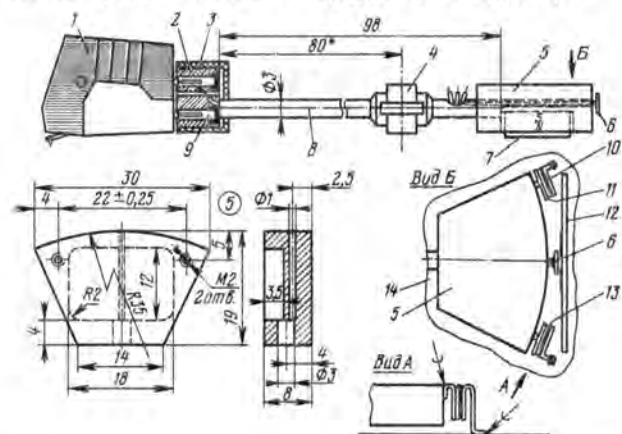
Звукоиндуктор: 1 — головка ГЗМ-003; 2 — пластина, стеклотекстолит фольгированный; 3 — колпак, эбонит; 4 — подвес карданный, резина НО68-1; 5 — противовес, ЛС39-1; 6 — пластина датчика положения тонарма, ЛС39-1; 7 — магнит постоянный ферритовый 25А; 8 — трубка тонарма, никель; 9 — гнездо, 4 шт., паять к дет. 2; 10 — пластина демпфера неподвижная, Л62-Т, паять к дет. 14; 11 — пластина демпфера подвижная, Л62-Т, паять к дет. 5; 12 — плата датчика положения тонарма; 13 — эпоксидная смола; 14 — каретка
